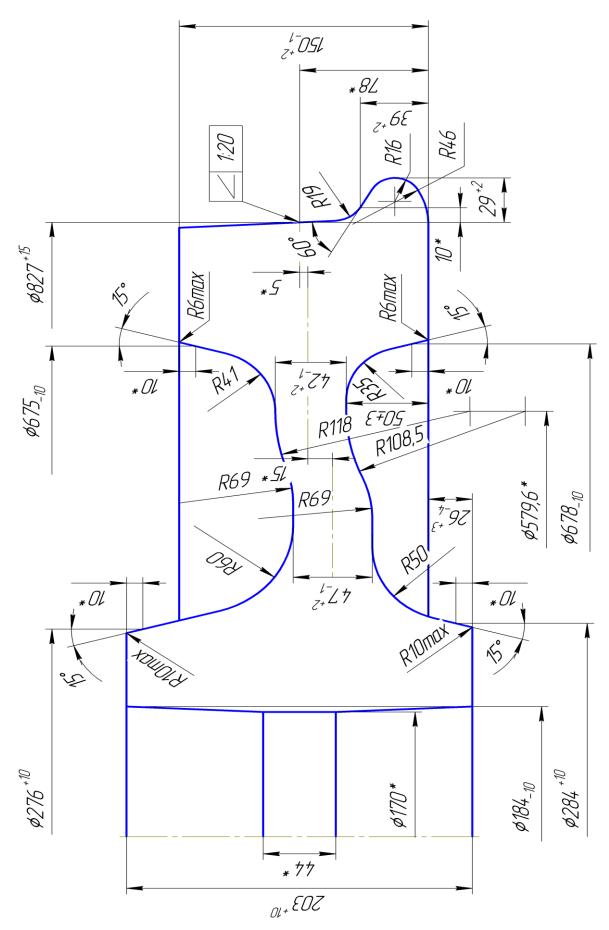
Колесо без механической обработки (после проката) \varnothing 827 мм, под чистовое \varnothing 813 мм, чертеж №КР-0017-16. Масса колеса - 453 кг.
